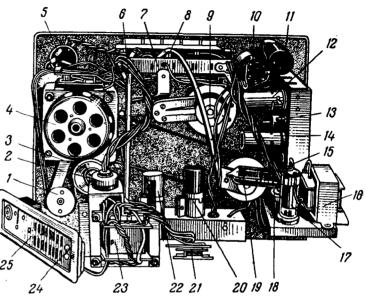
Расположение деталей лентопротяжного механнзма и усилителя.
